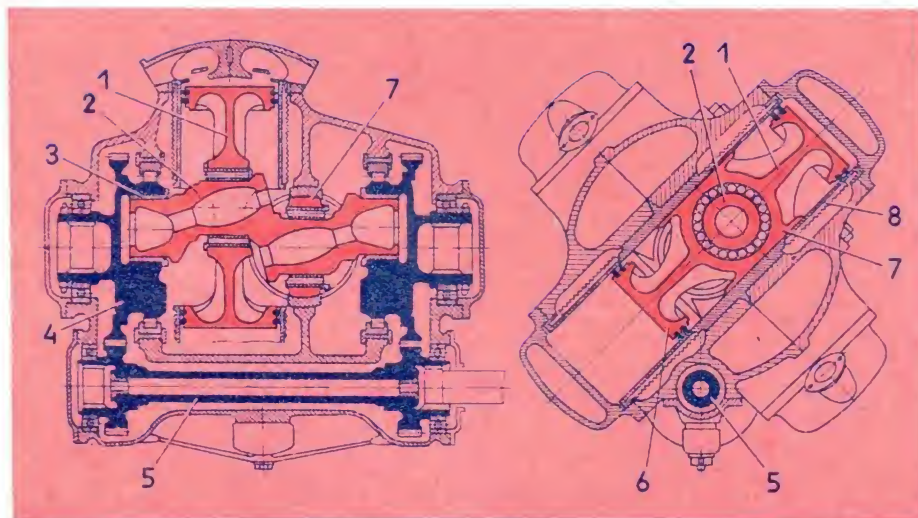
Принципиальное устройство бесшатунного двигателя: 1 — поршневой шток; 2 — коленчатый вал; 3 — подшипник кривошипа; 4 — кривошип; 5 — вал отбора мощности; 6 — поршень; 7 — ползун штока; 8 — цилиндр.
